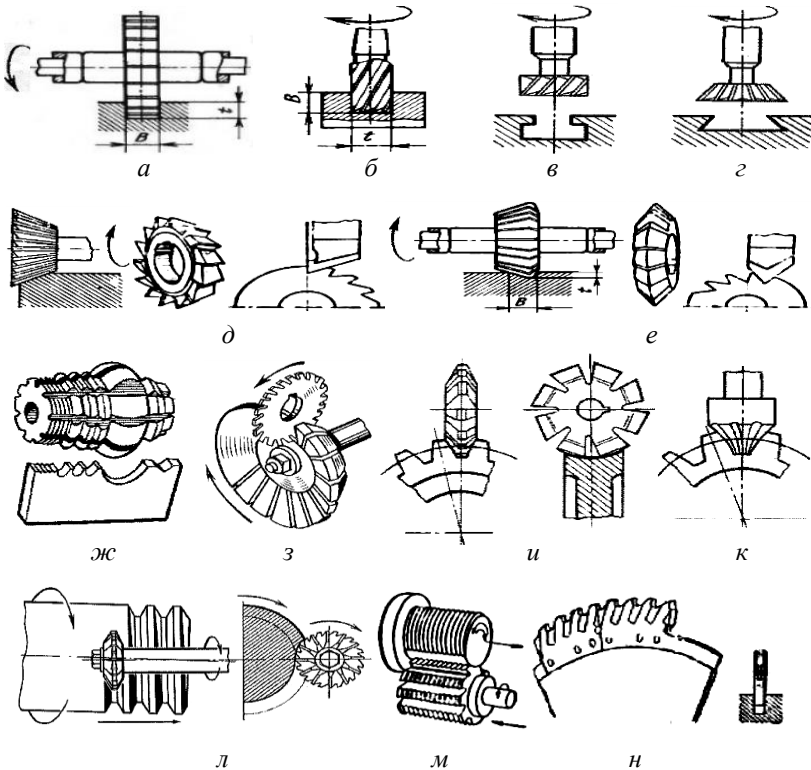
Получение пазов, канавок и шлицев фрезами:
